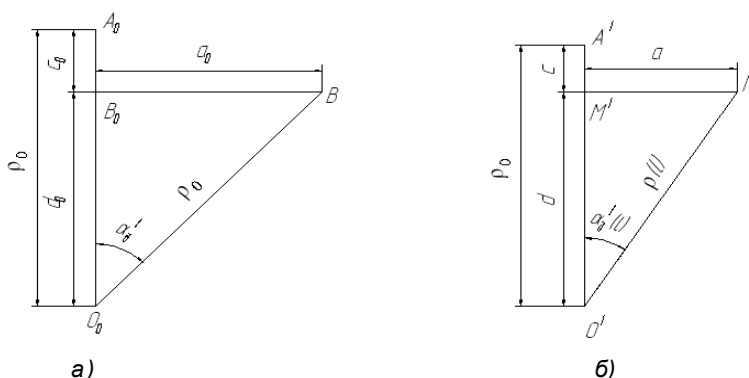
Заготовка в исходном положении (вид сверху)
